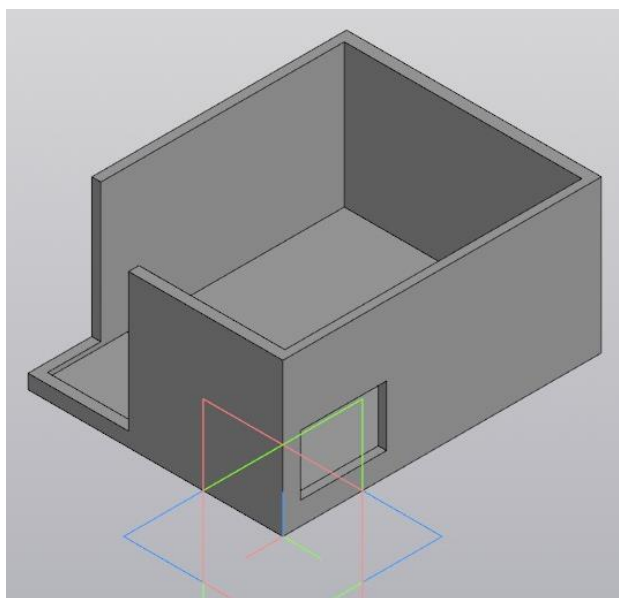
3D чертёж корпуса Smart устройства «Умный дом»
